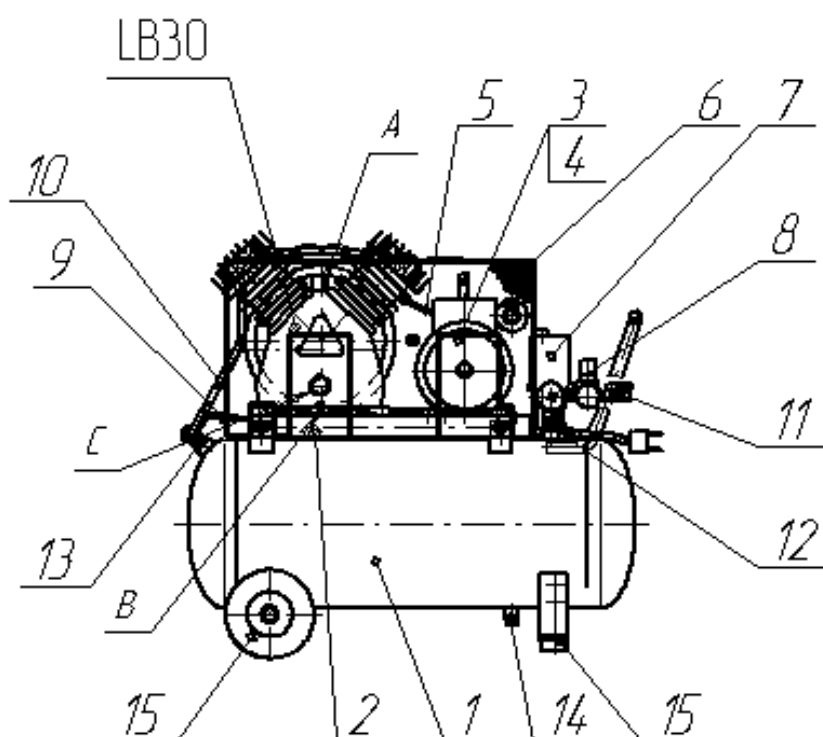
Общий вид компрессора СБ4/С-50.LB30, СБ4/С-50.LB30А
